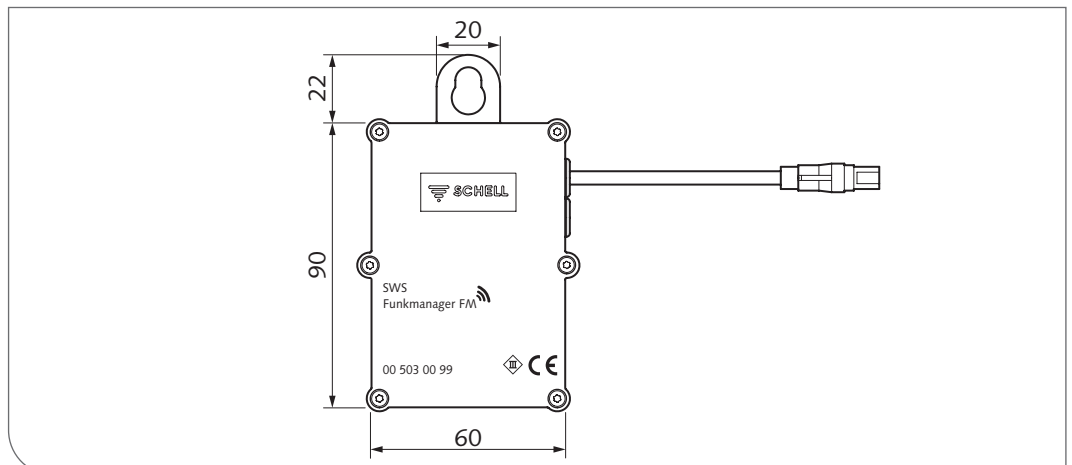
Gestor inalámbrico SWS FM. Dimensiones
